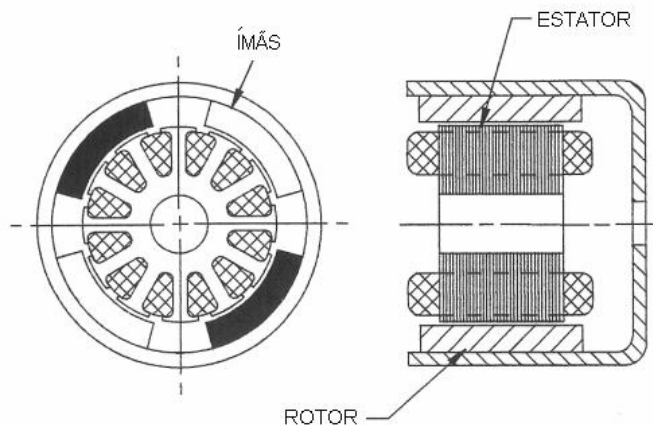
Motor de rotor externo (HENDERSHOT; MILLER, 1994)
